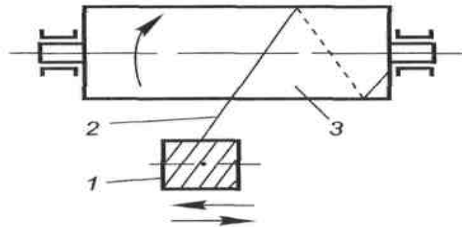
Схема намотування: 1 – котушка; 2 – наповнювач; 3 – оправка
